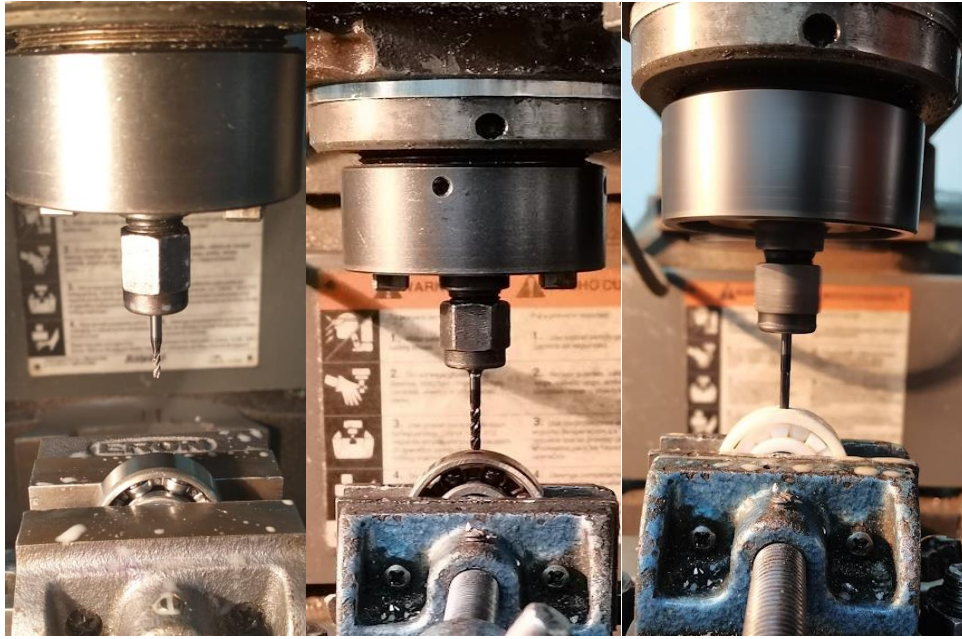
Manufactura de fallos en la pista exterior (Autoría Propia).
